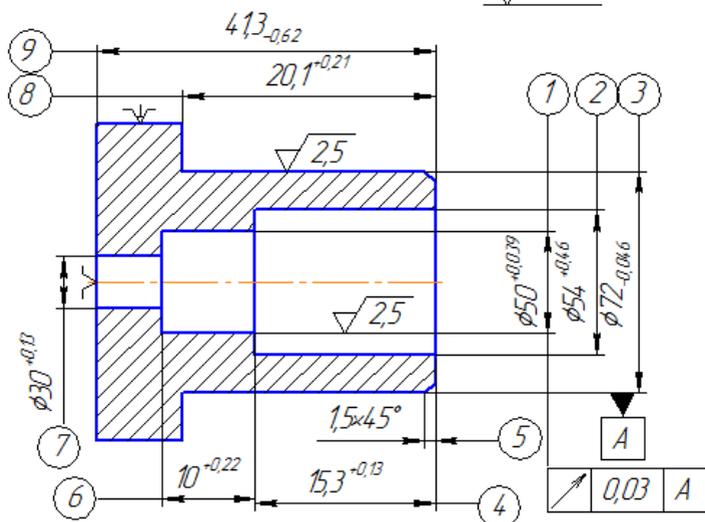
Эскизы заготовки из стали 20Х и токарной операции обработки детали «Крышка» на станке модели 1П420ПФ30 (1716ПФ3)
